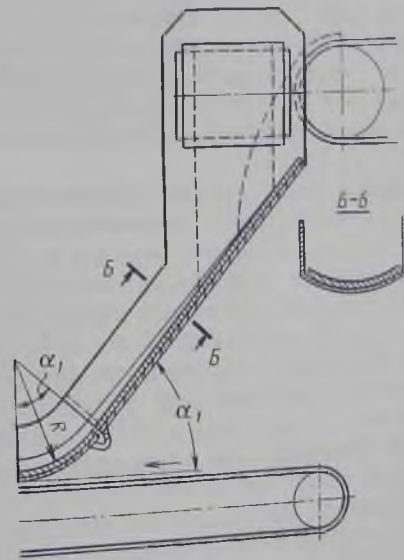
Схема загрузочного устройства для мелкокусковых руд
